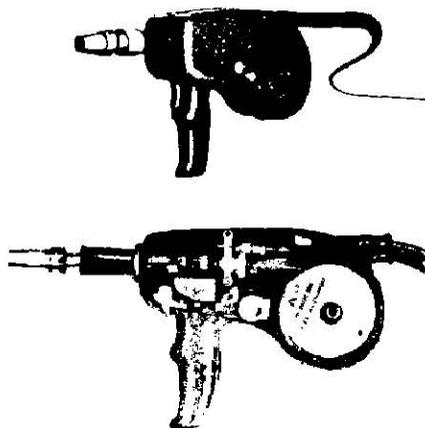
(Arriba) Pistola para soldadura MIG; (abajo) corte seccional para mostrar rollo de electrodo de 4 pulg de diámetro en la pistola.
